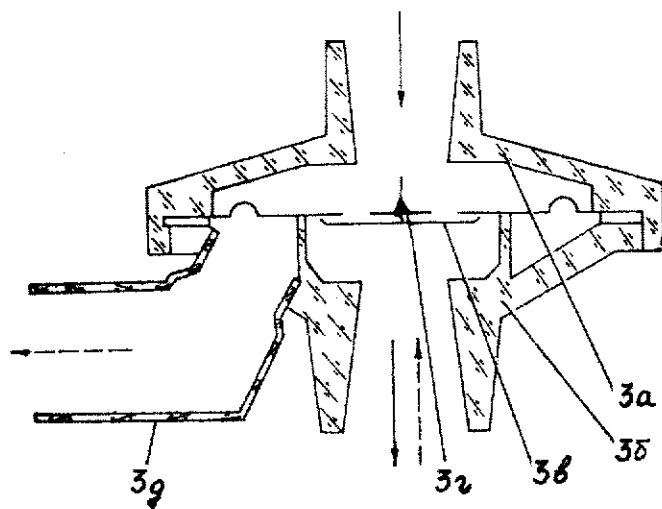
Схематическое изображение нереверсивного клапана для детей с патрубком выдоха:
